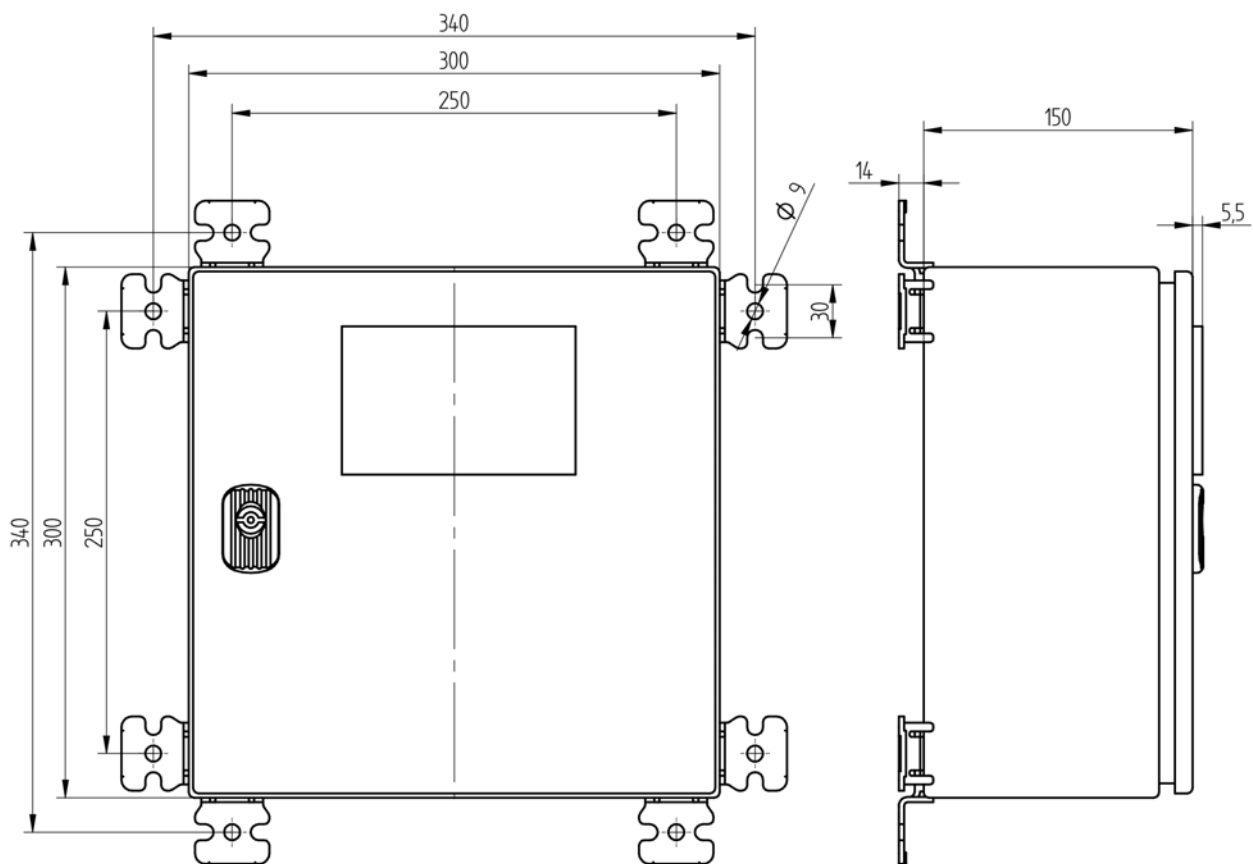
Plan coté LT3-F dans un boîtier acier inox avec supports muraux vertical/horizontal et UI300-LT-V2 avec couverture supplémentaire pour IP65 (dimensions en mm)
